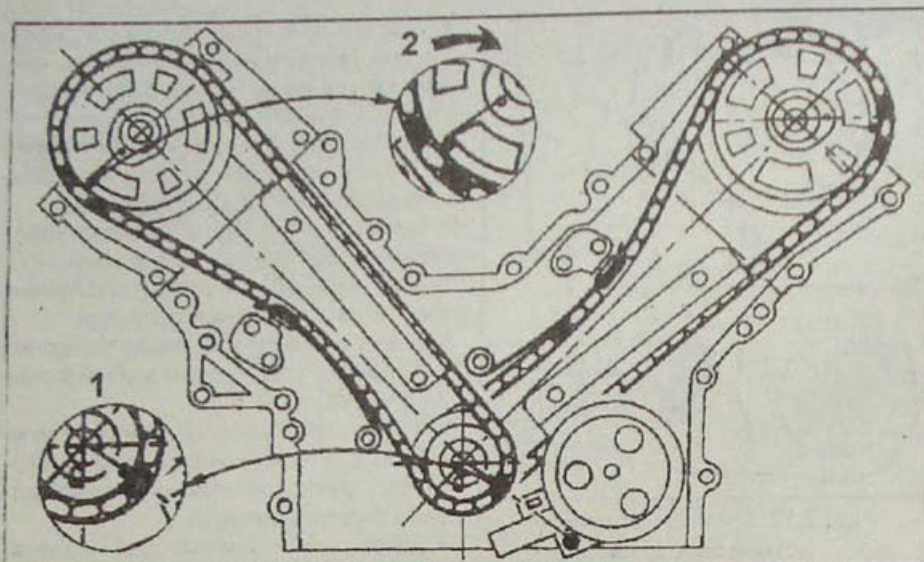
Положение распределительного вала передней головки цилиндров: 1 — шпонка коленчатого вала, повернутая в сторону к передней секции блока цилиндров; 2 — метка на звездочке распределительного вала, находящаяся между двумя метками цепи
